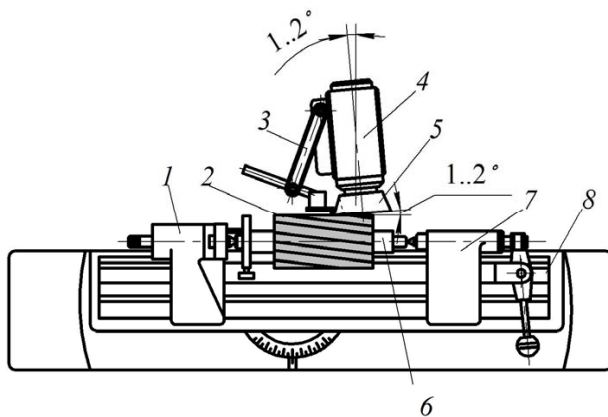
Наладка заточного станка для заточки цилиндрической фрезы с винтовыми стружечными канавками: 1 – передняя бабка; 2 – фреза; 3 – упорка; 4 – шлифовальная головка; 5 – шлифовальный круг; 6 – центровая оправка; 7 – задняя бабка; 8 – стол
